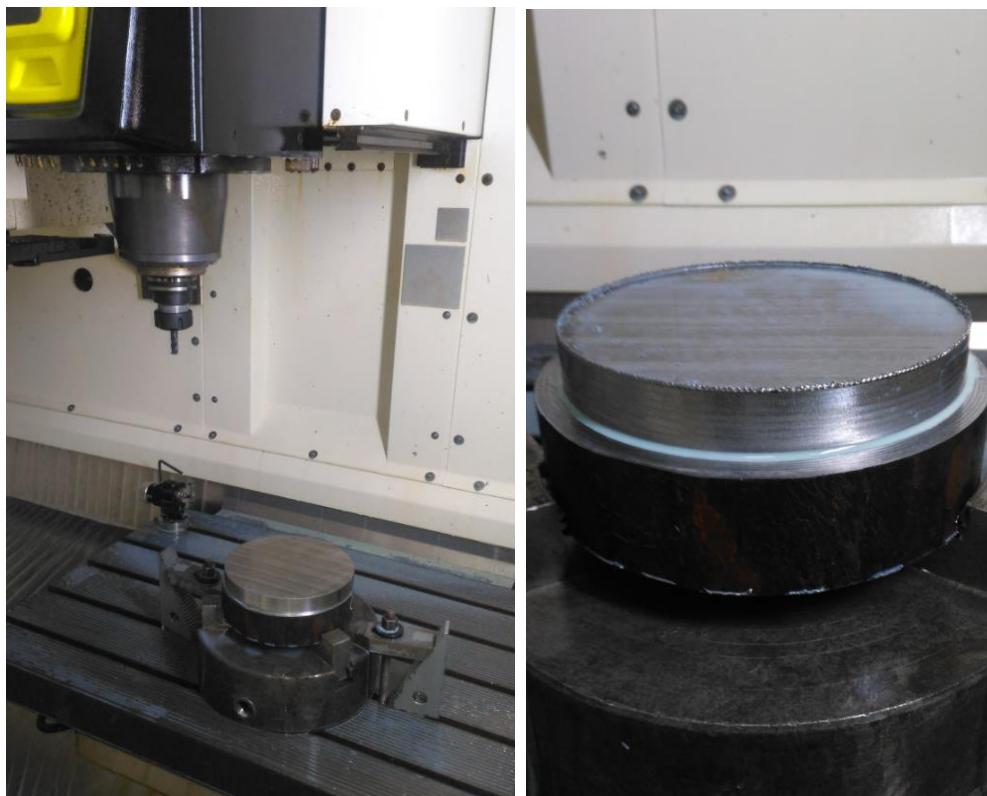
Проведение экспресс-испытаний опытных образцов фрез
